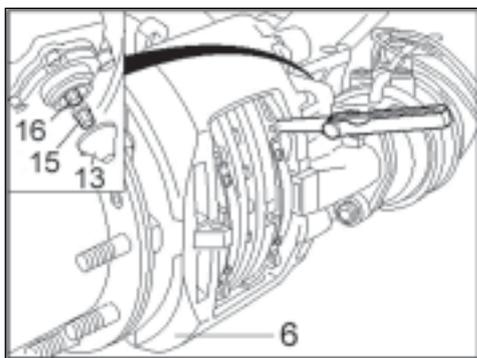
Проверка зазора между тормозной колодкой и упорами
